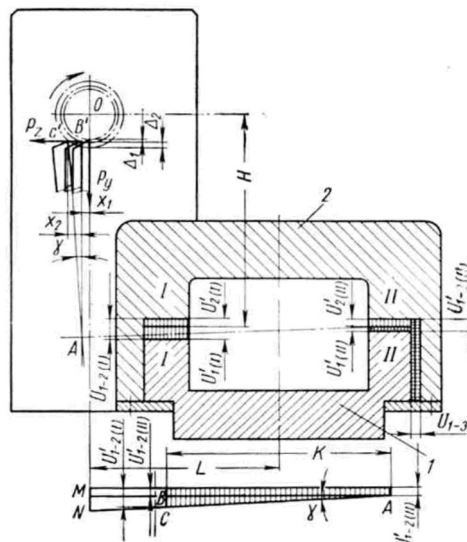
Схема визначення погрішності розміру деталі при обробці різцем з револьверного супорта: 1 — станина верстата; 2 — каретка револьверного супорта; I — передні горизонтальні направляючі станини і каретки; II — задні горизонтальні направляючі станини і каретки.
